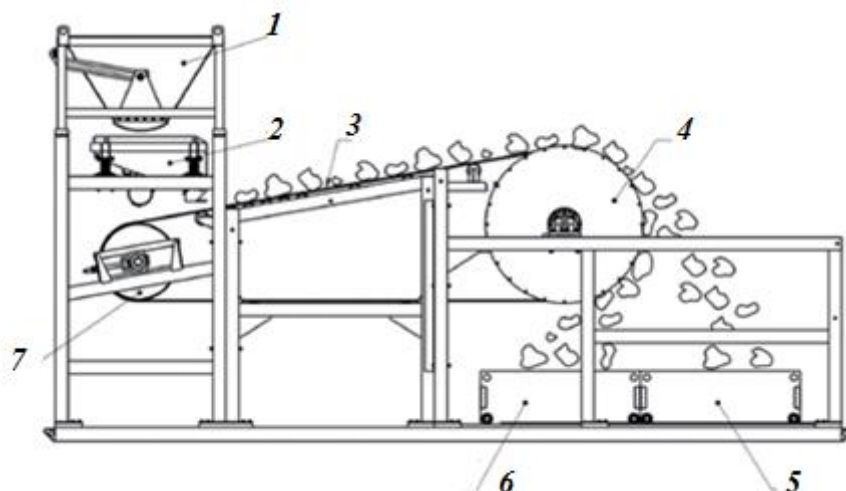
Схема магнитной рудоразборки: 1-приёмный бункер, 2- виброподача; 3- транспортёрная лента; 4- магнитный барабан; 5- бункер пустой породы; 6-бункер для магнитной фракции; 7- натяжной барабан.
